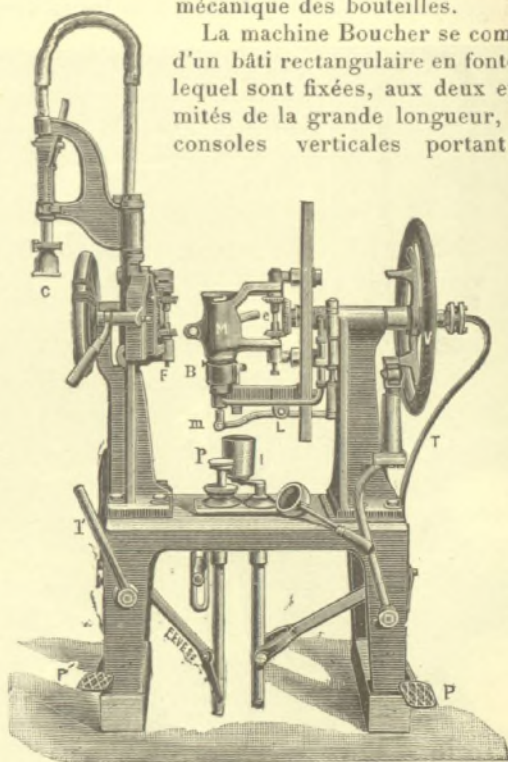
Machine C. Boucher pour la fabrication mécanique des bouteilles.
